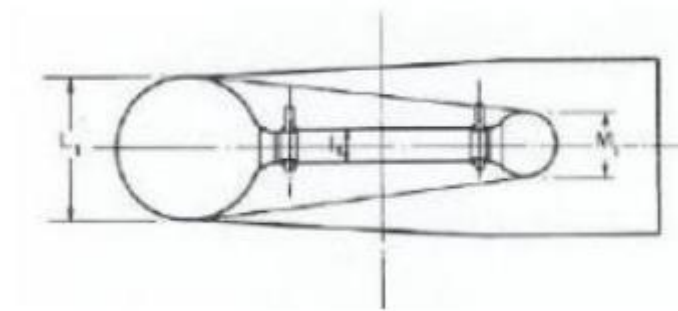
Resta dimensions de la carcassa espiral [5]
